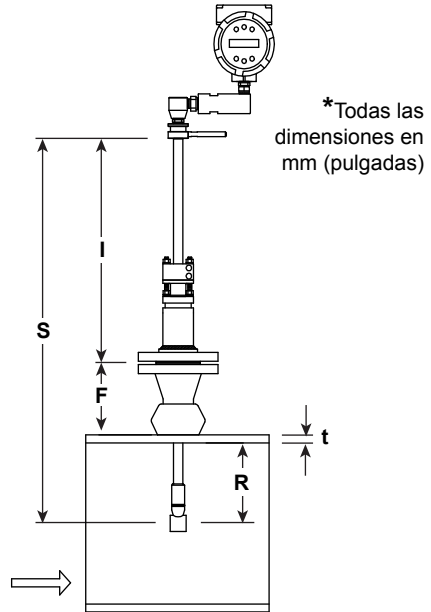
Cálculo de inserción (medidor si herramienta de inserción)
